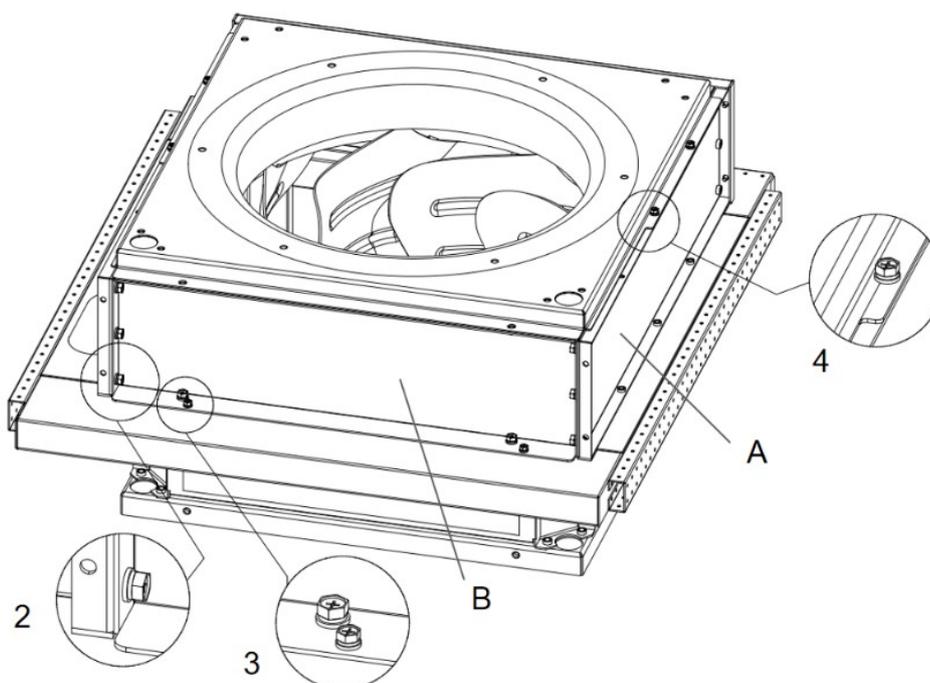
Кронштейн подсоединен и вентилятор закреплен
